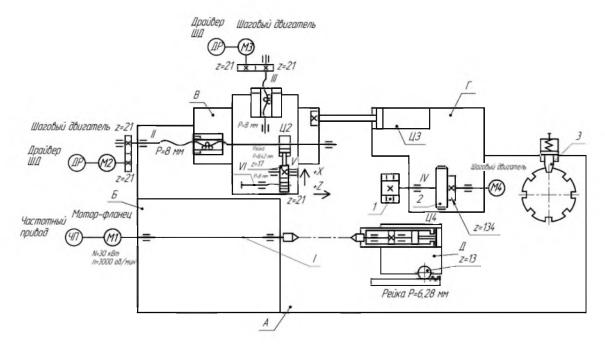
Модернизированная кинематическая схема станка с ЧПУ 1725МФ3
